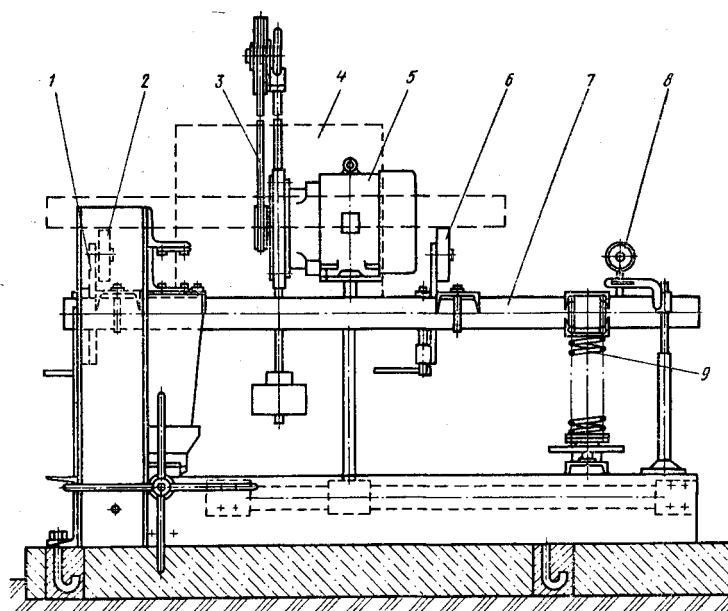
Универсальный балансировочный станок для динамической балансировки
